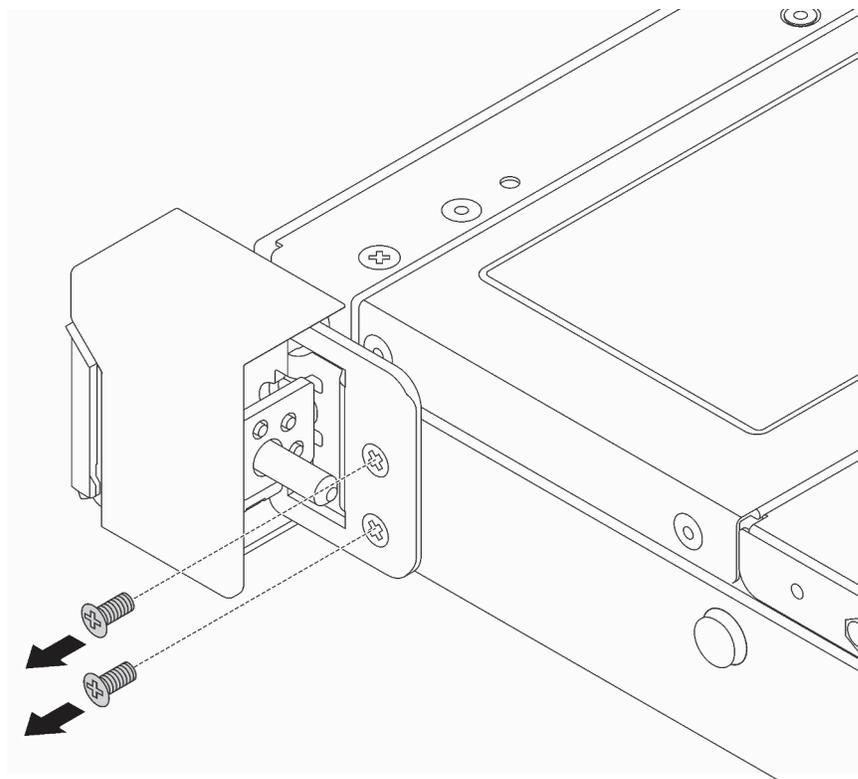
Entfernen der Schrauben der Rack-Verriegelung
